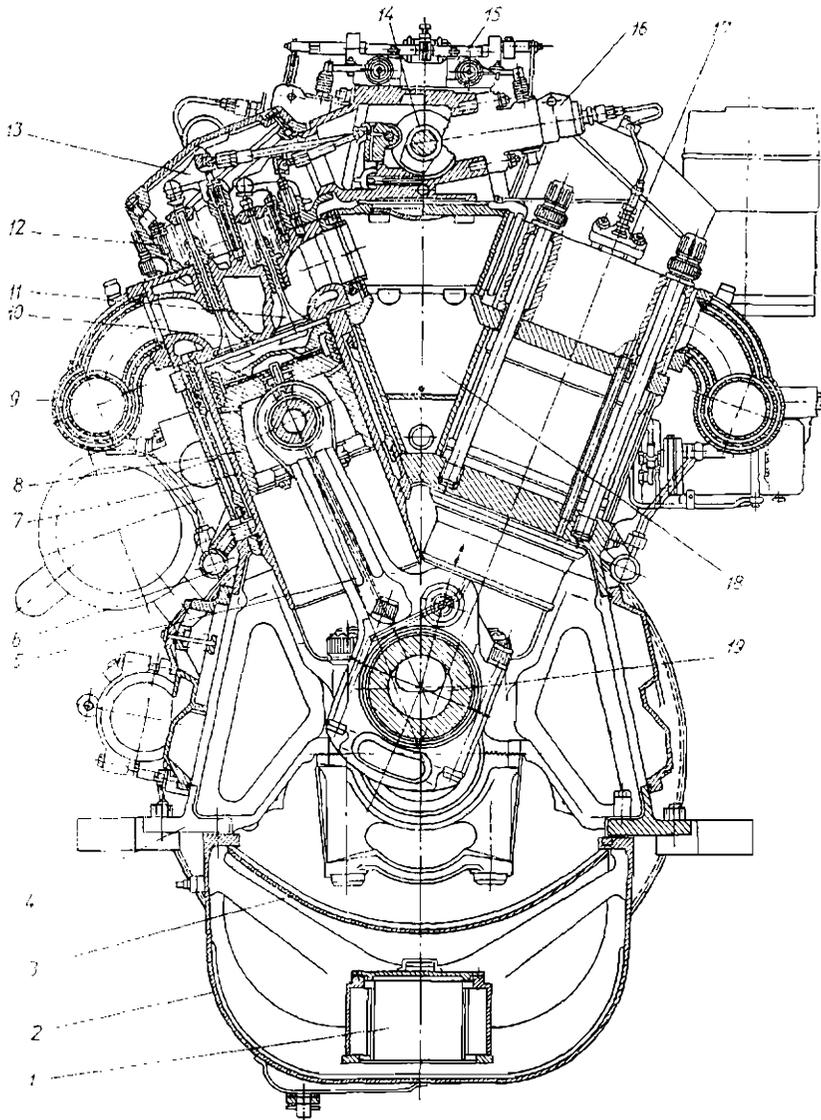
Поперечный разрез дизеля 3А-6Д49:
